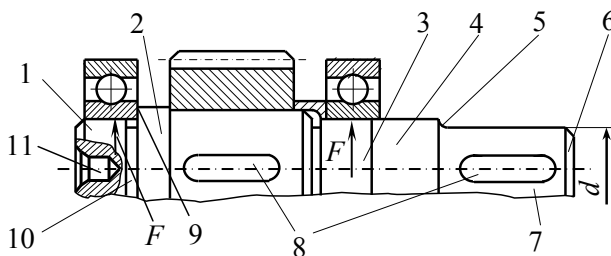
Элементы ступенчатой конструкции вала:
